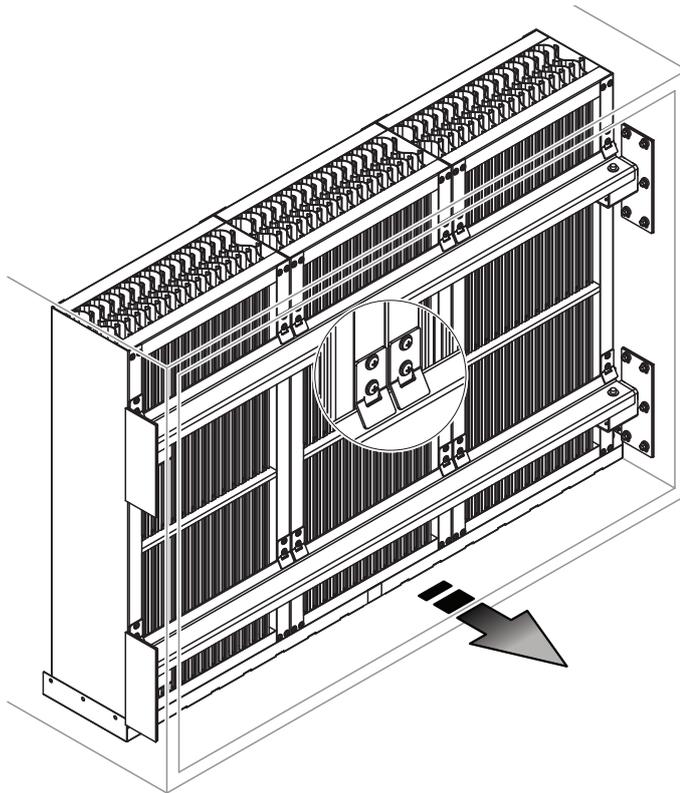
Installazione delle lamiera di protezione inferiori
